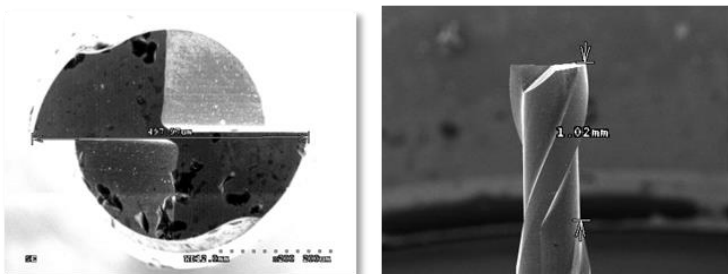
Beispiel für Werkzeuggröße in der Mikrobearbeitung
